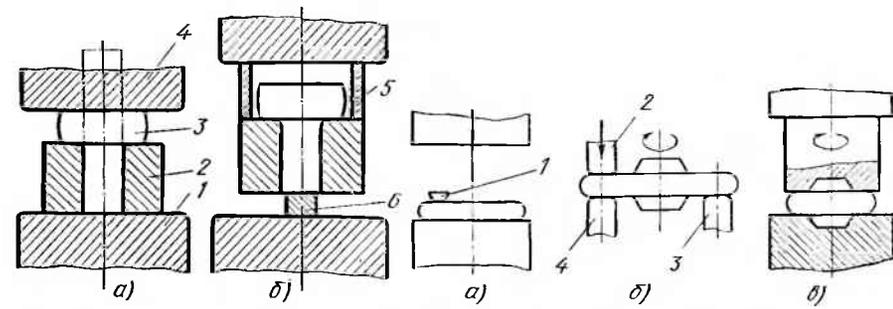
Схемы высадки в штампе (*a*) и удаления заготовки (*б*):
